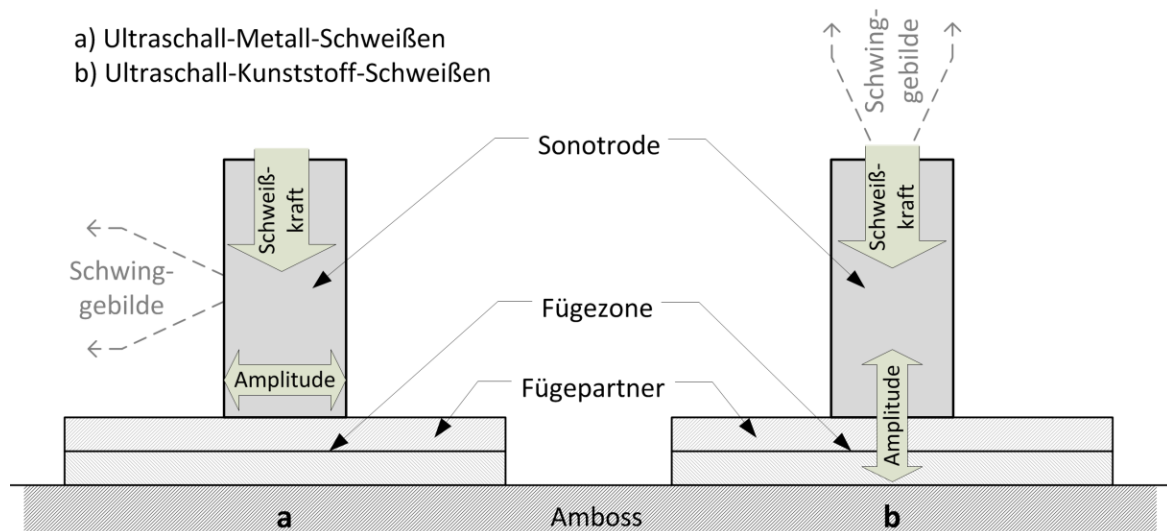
Unterschied materialabhängiger Ultraschallschweißverfahren: Metall-Schweißen (links); Kunststoff-Schweißen (rechts)
